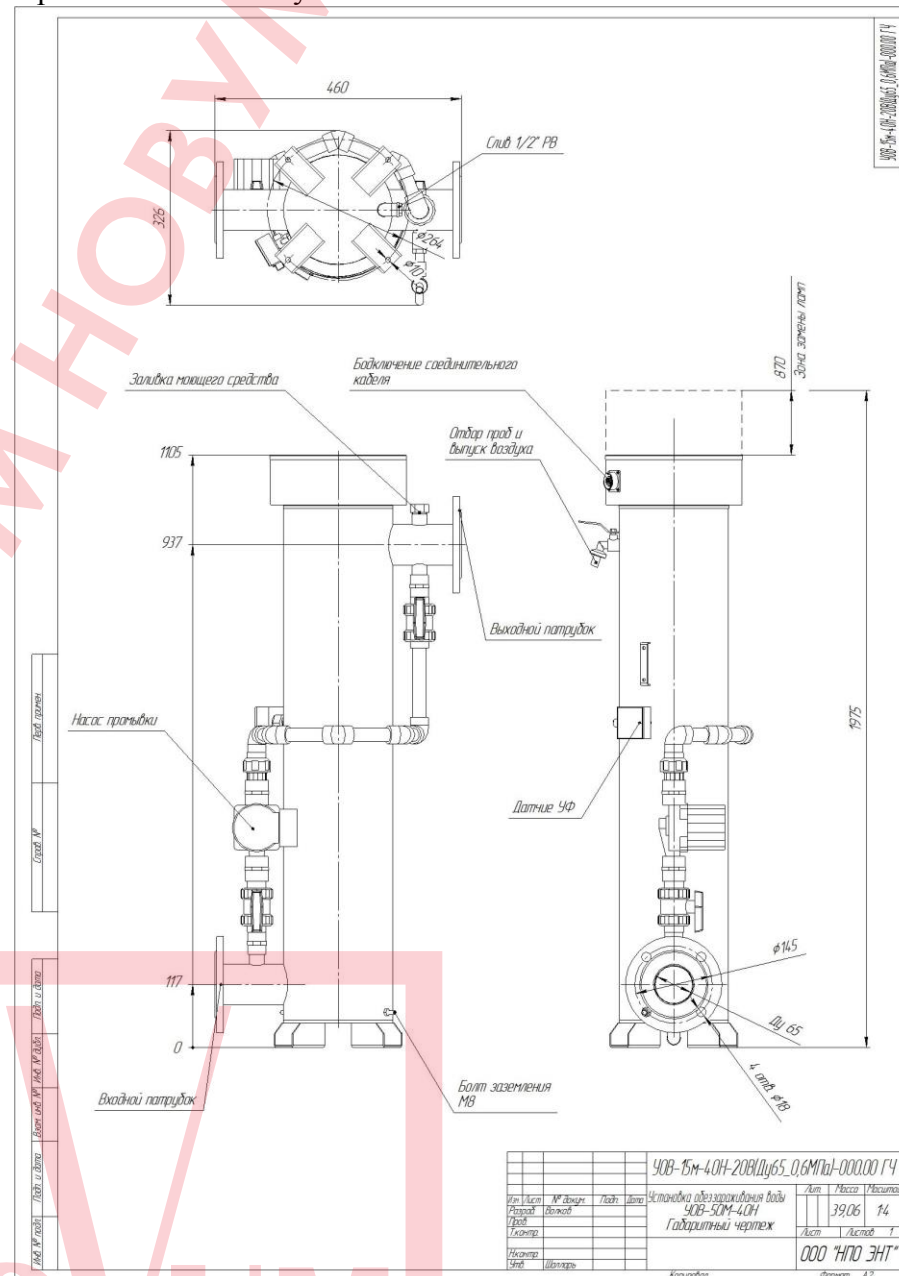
УОВ-15м-40Н. Габаритный чертеж
